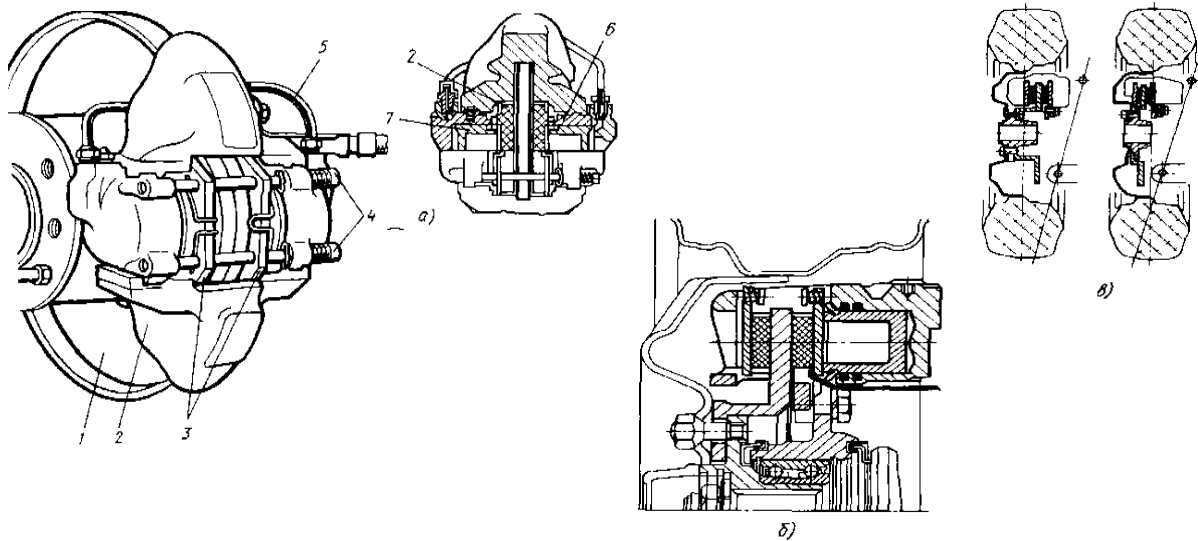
Дисковые тормозные механизмы: а – с неподвижной скобой; б – с плавающей скобой; в – схема установки, неподвижной и плавающей скоб; 1 – тормозной диск; 2 – скоба; 3 – тормозные колодки; 4 – пальцы установки колодок; 5 – соединительная трубка; 6 – резиновое кольцо; 7 – поршни
